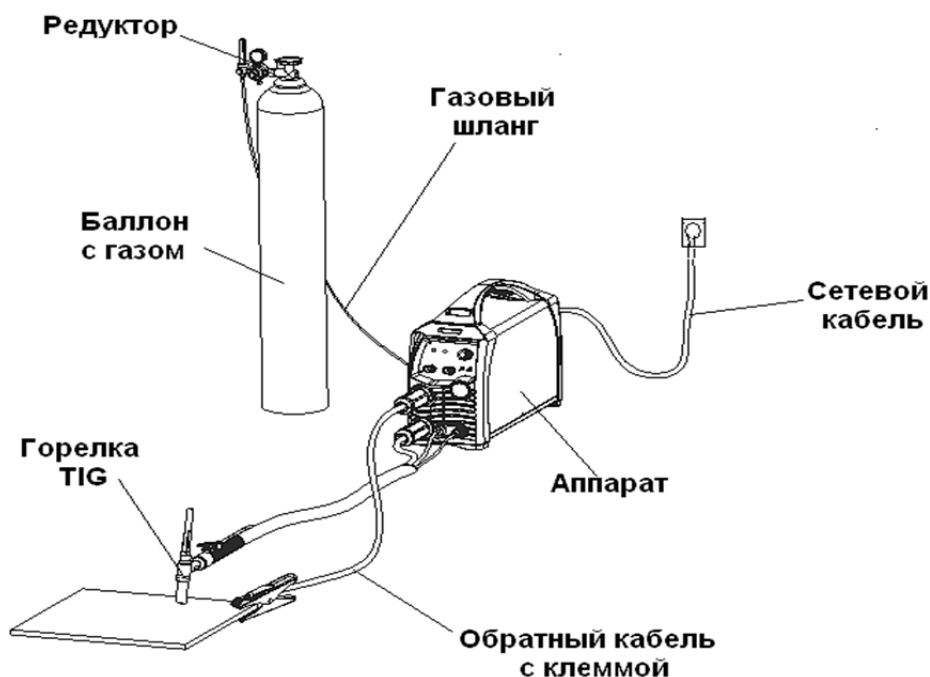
Схема подключения аппарата для TIG сварки
